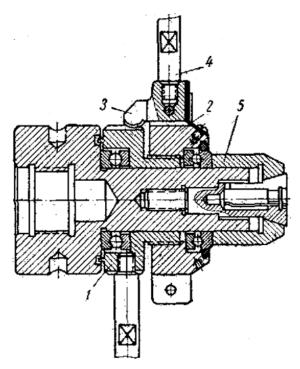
Цанговый механизм с возможностью зажима и разжима заготовки на ходу
